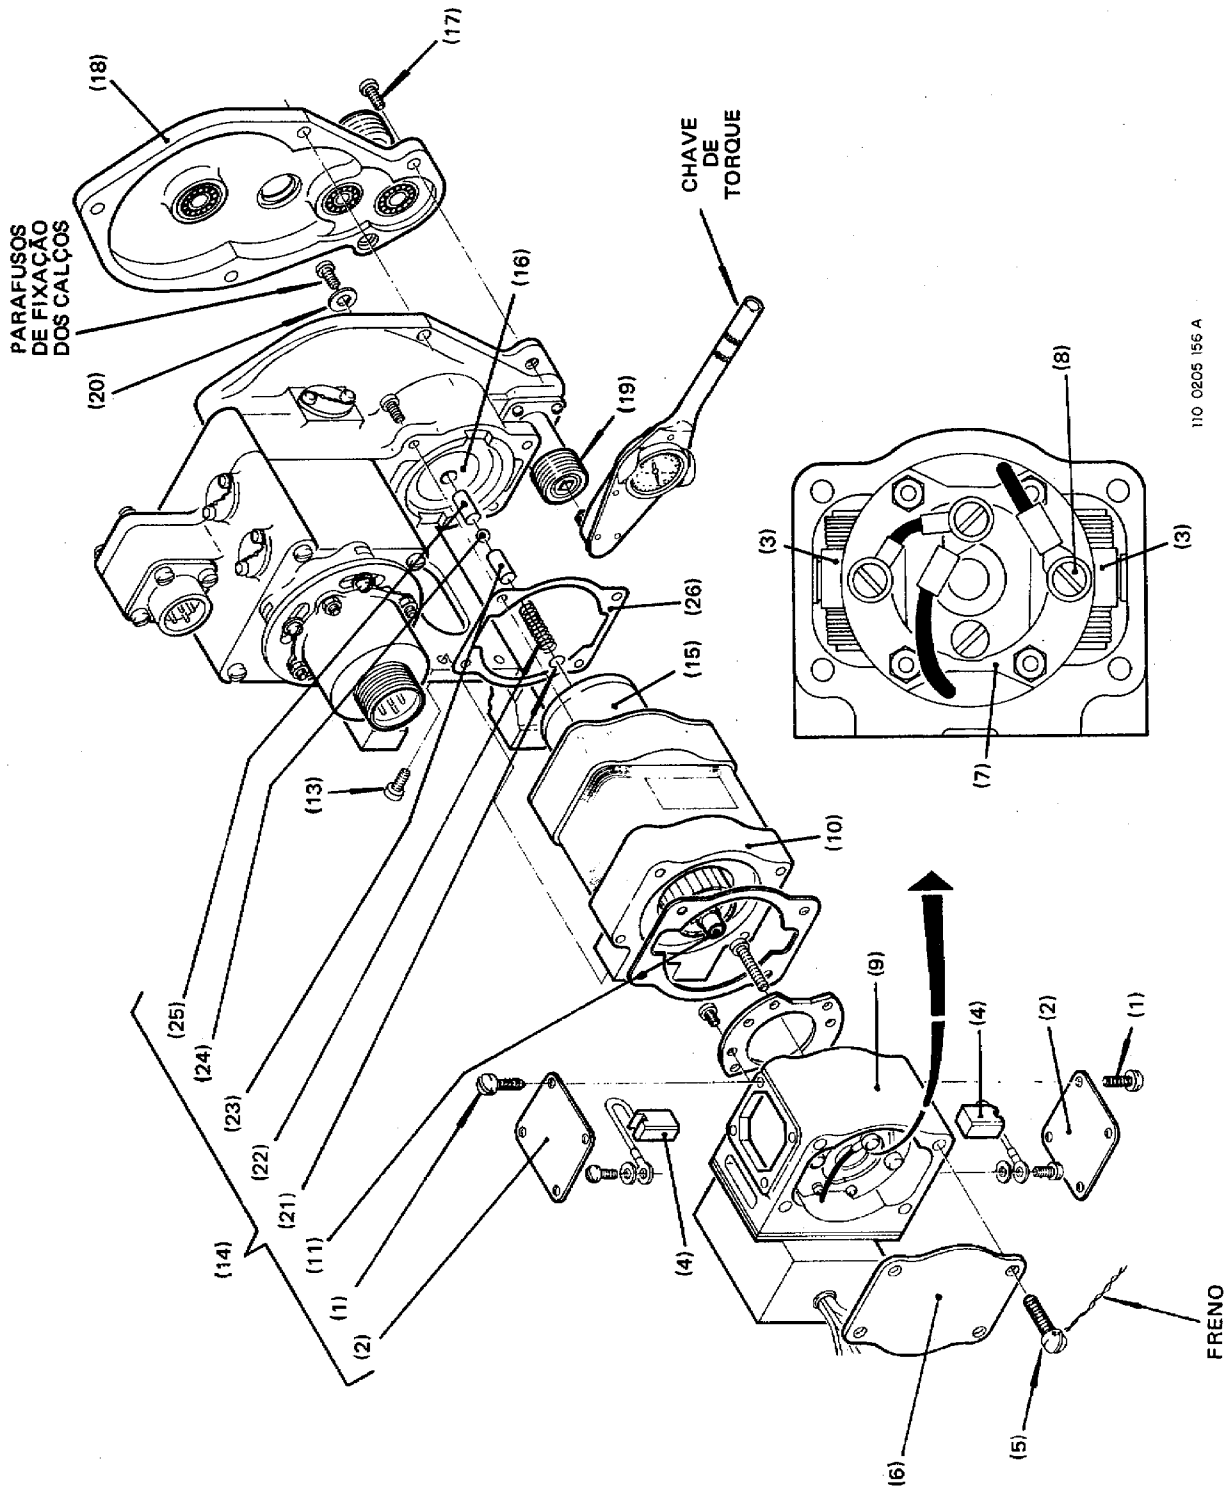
Inspeção de Bancada do Motor Atuador do Flape
